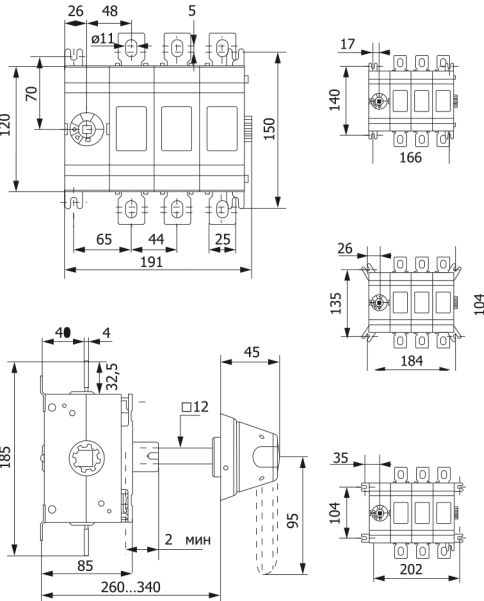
Габаритные и установочные размеры рубильников 315-400А
